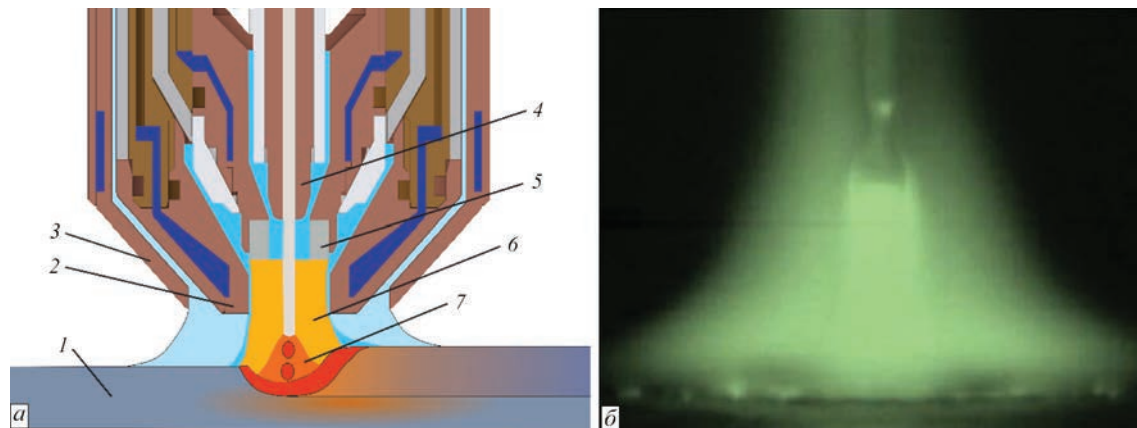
Технологическая схема процесса (а) и фотография совместного действия сжатой дуги и дуги с плавящимся электродом (б) гибридной плазменно-дуговой сварки: 1 — свариваемый образец; 2 — плазмообразующее сопло; 3 — защитное сопло; 4 — мундштук плавящегося электрода; 5 — трубчатый электрод плазматрона (анод); 6 — сжатая дуга прямого действия; 7 — дуга плавящегося электрода
